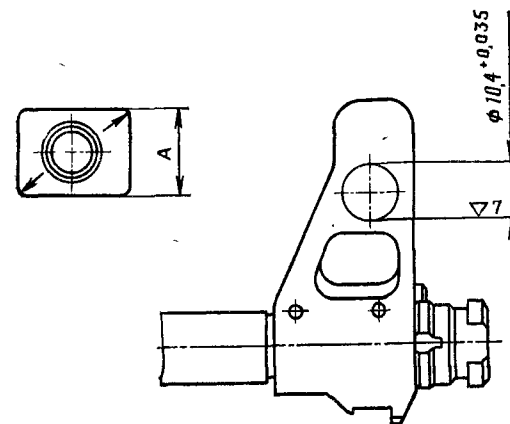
Обработка отверстия для основания в колодке мушки автомата Калашникова
